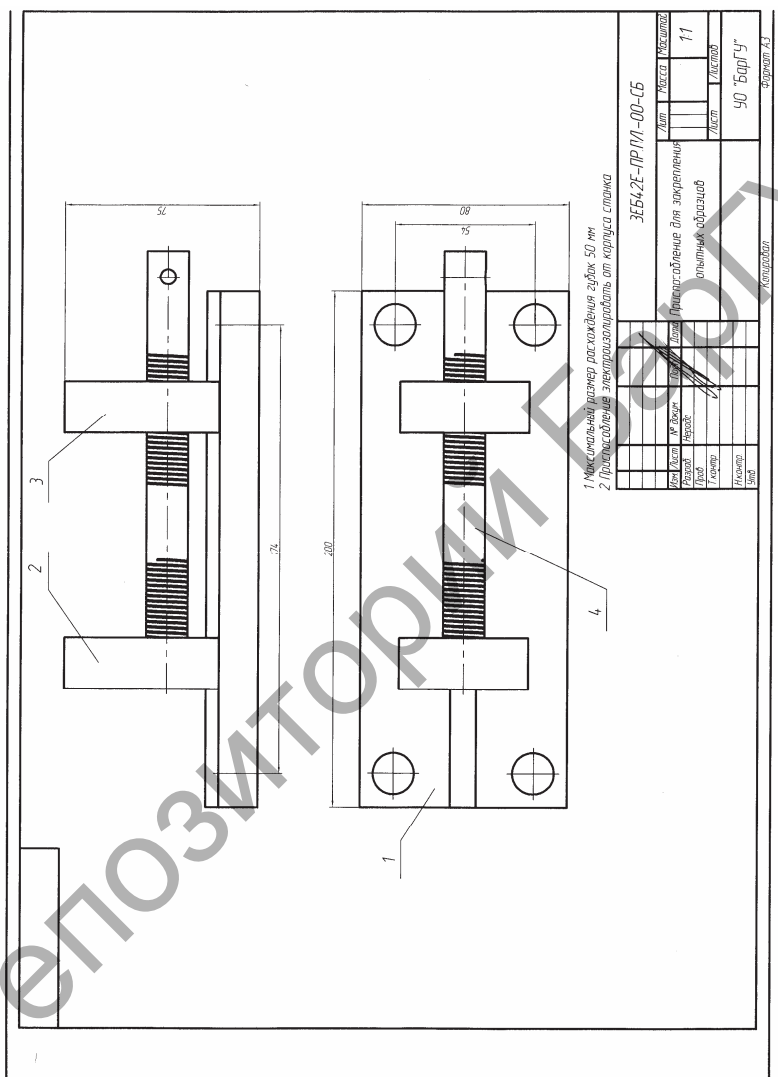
Принадлежность для закрепления опытных образцов
